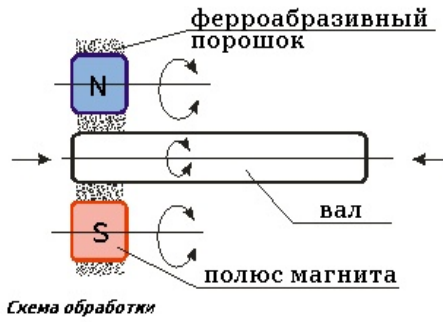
Схема установки для MAO наружных цилиндрических поверхностей:
